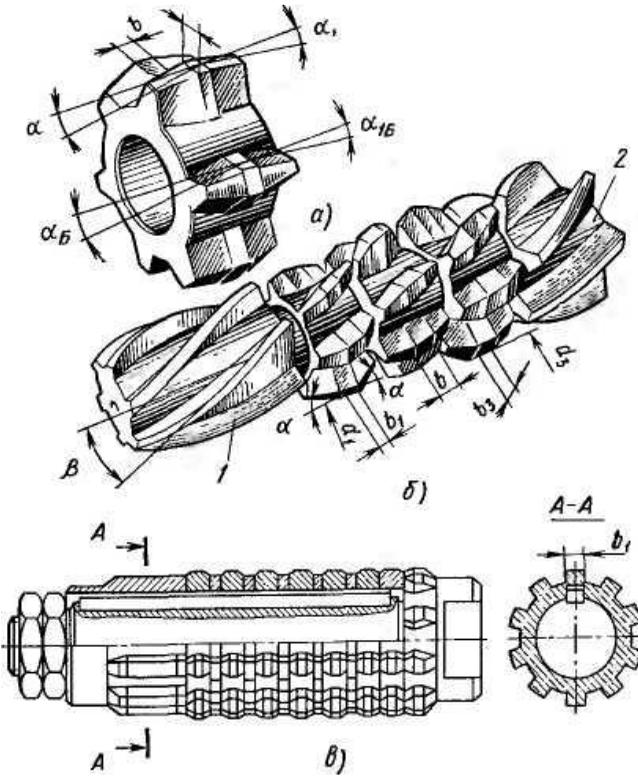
Дорни для обробки шліцевих валів: а – однозубий дорн; б – багатозубий гвинтовий дорн; в – багатозубий прямий дорн;
